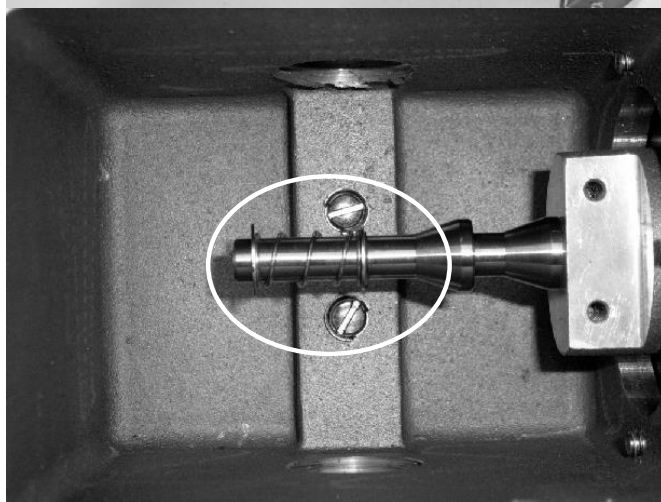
Узел переключателя в сборе, стопор пружины, пружины с шайбами и крепежные винты с шайбами.
